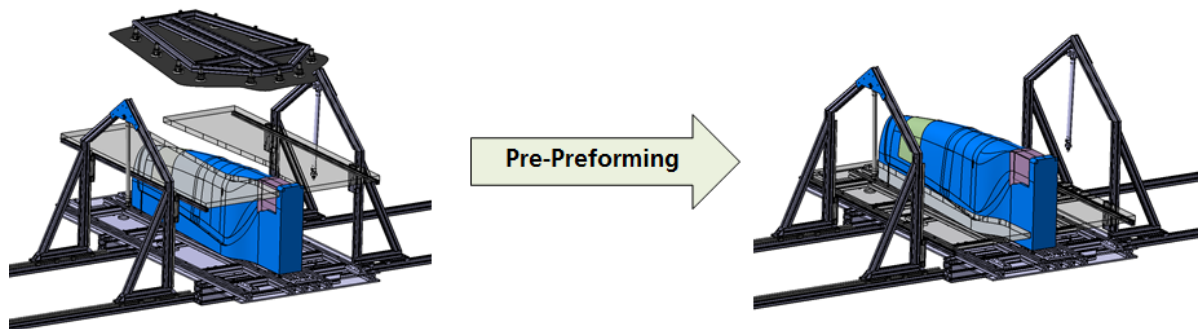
Flächige Auflage der Zuschnitte mit geführter Absenkmechanik
